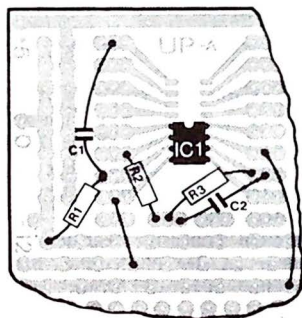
Die Schaltung aus Bild 5 auf dem Print.
